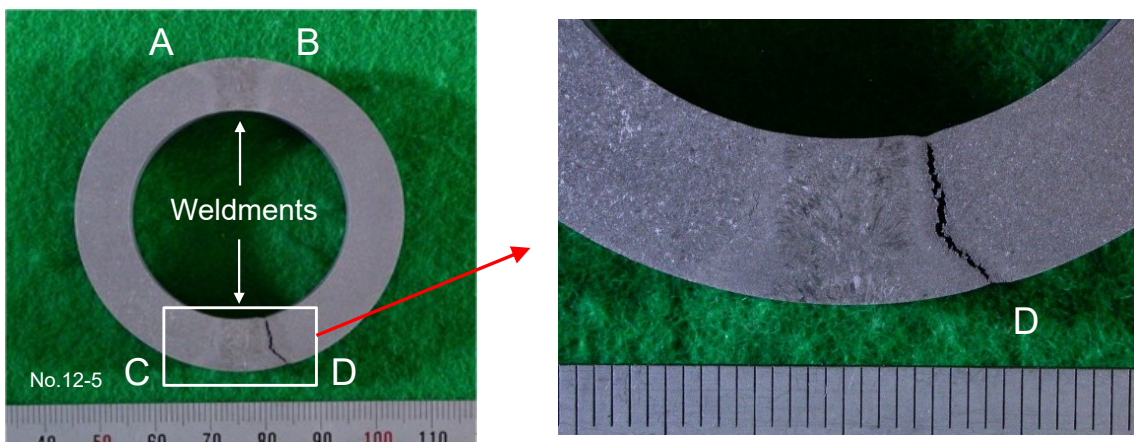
内圧クリープ試験体の破壊後の断面状況 (No. 12-5)
